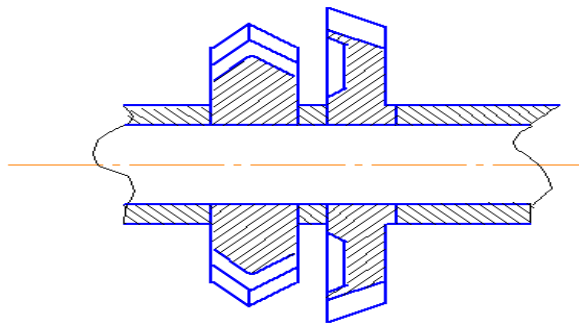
Збірна фреза для оброблення зуба розгортки
